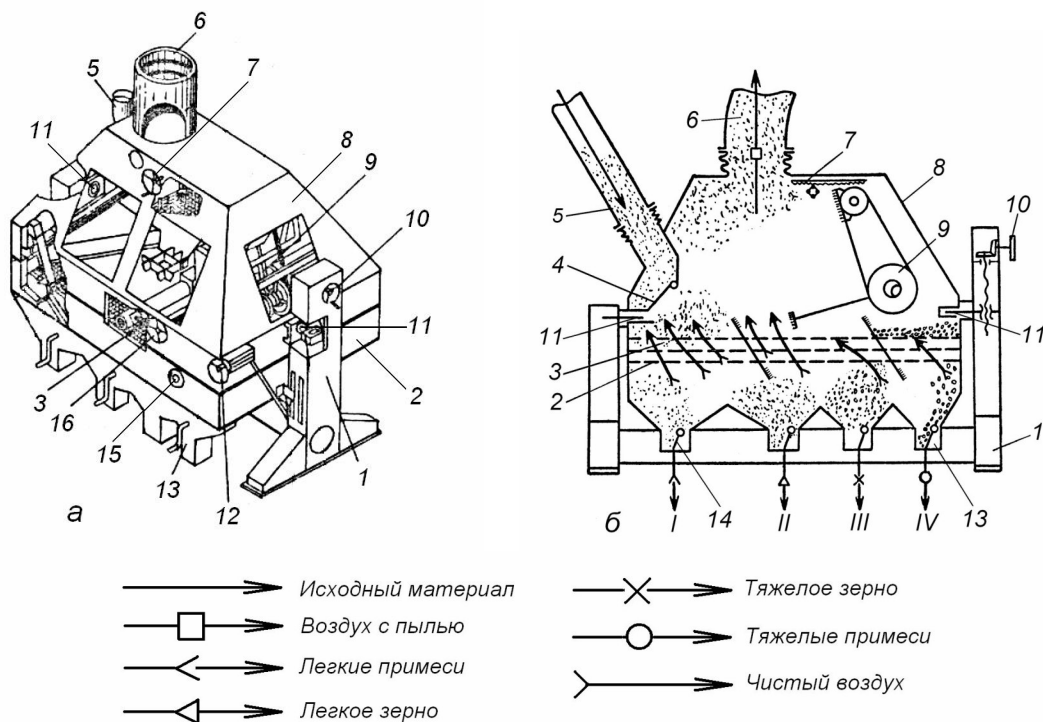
Пневматический сортировальный стол СПС-5: *а* – вид общий; *б* – схема технологическая; 1 – станина; 2 – стан; 3 – дека; 4 – клапан-питатель; 5 – загрузочная горловина; 6 – патрубок; 7 – механизм регулировки расхода воздуха; 8 – зонт; 9 – механизм вибропривода деки; 10 – механизм регулировки продольного угла наклона; 11 – шаровые опоры; 12 – механизм регулировки поперечного угла наклона; 13 – приёмники зерна; 14 – вакуумный клапан; 15 – пробоотборник; 16 – механизм управления вариатором.
